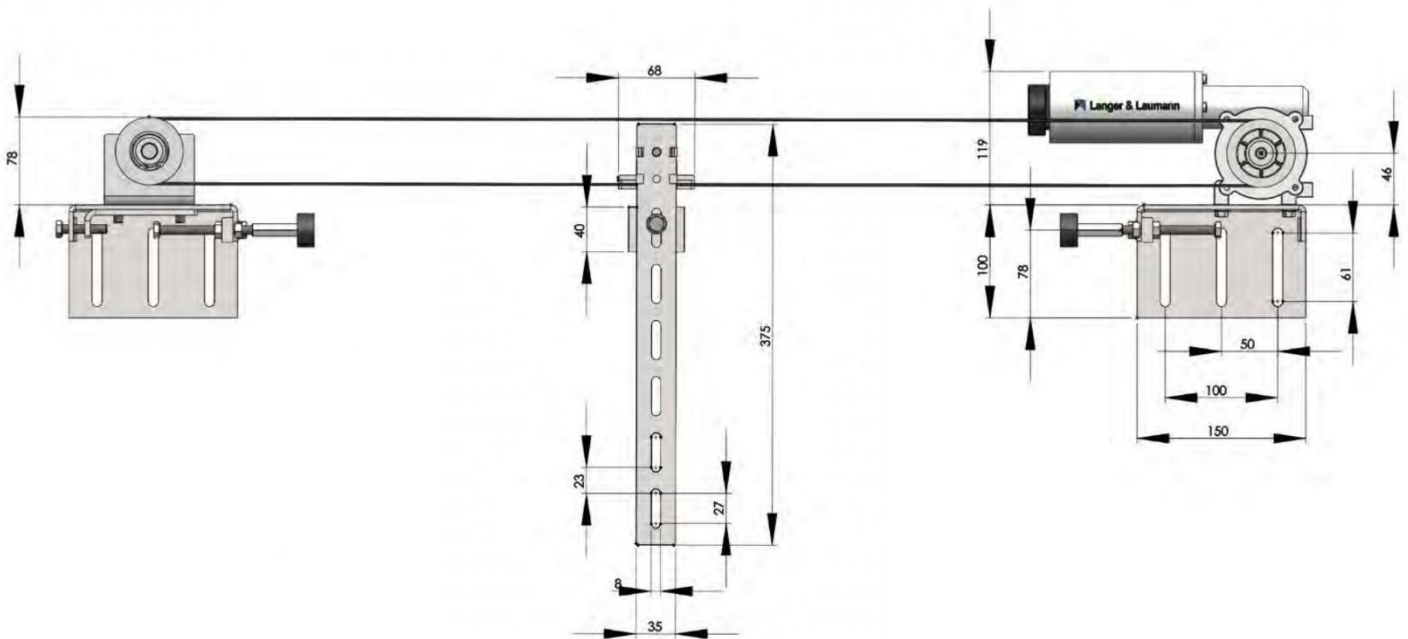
TSG Universalumbausatz - Bemaßung Front
